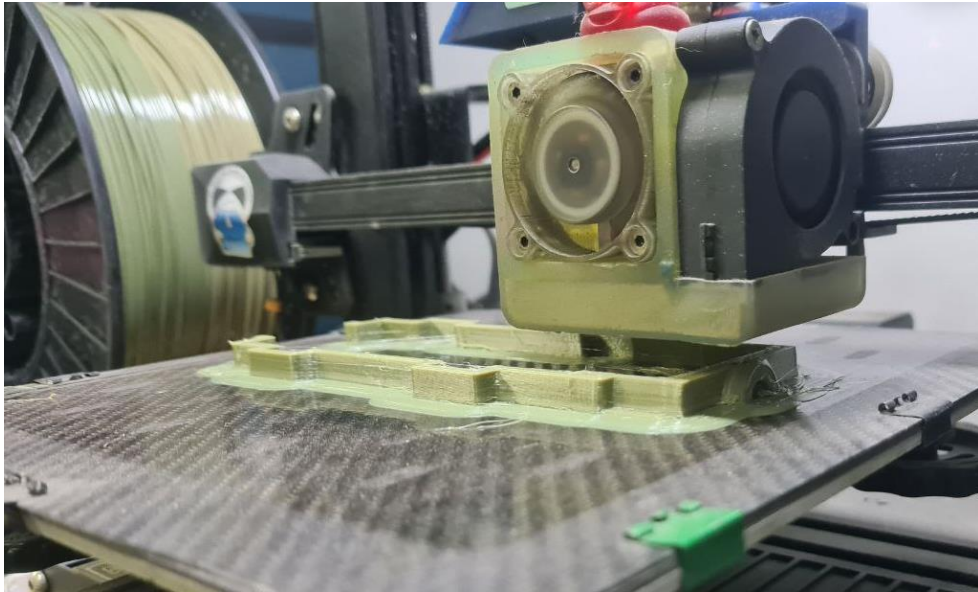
Друк корпусу на 3Д принтері (частина 2)
